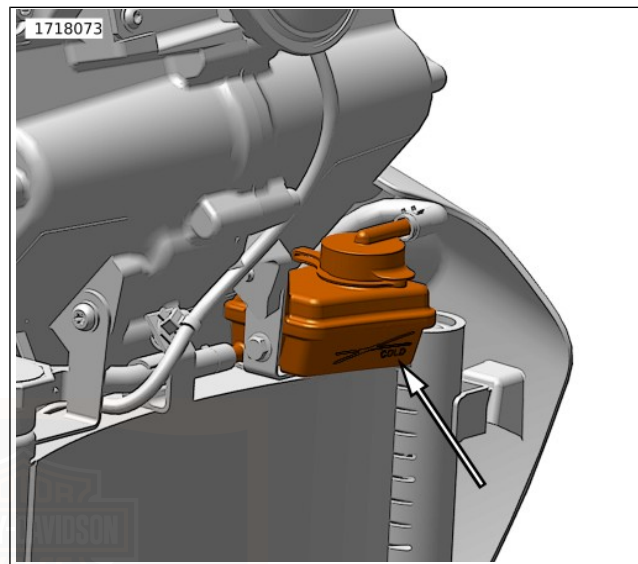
Kühlmittelstand, Markierung „COLD“
